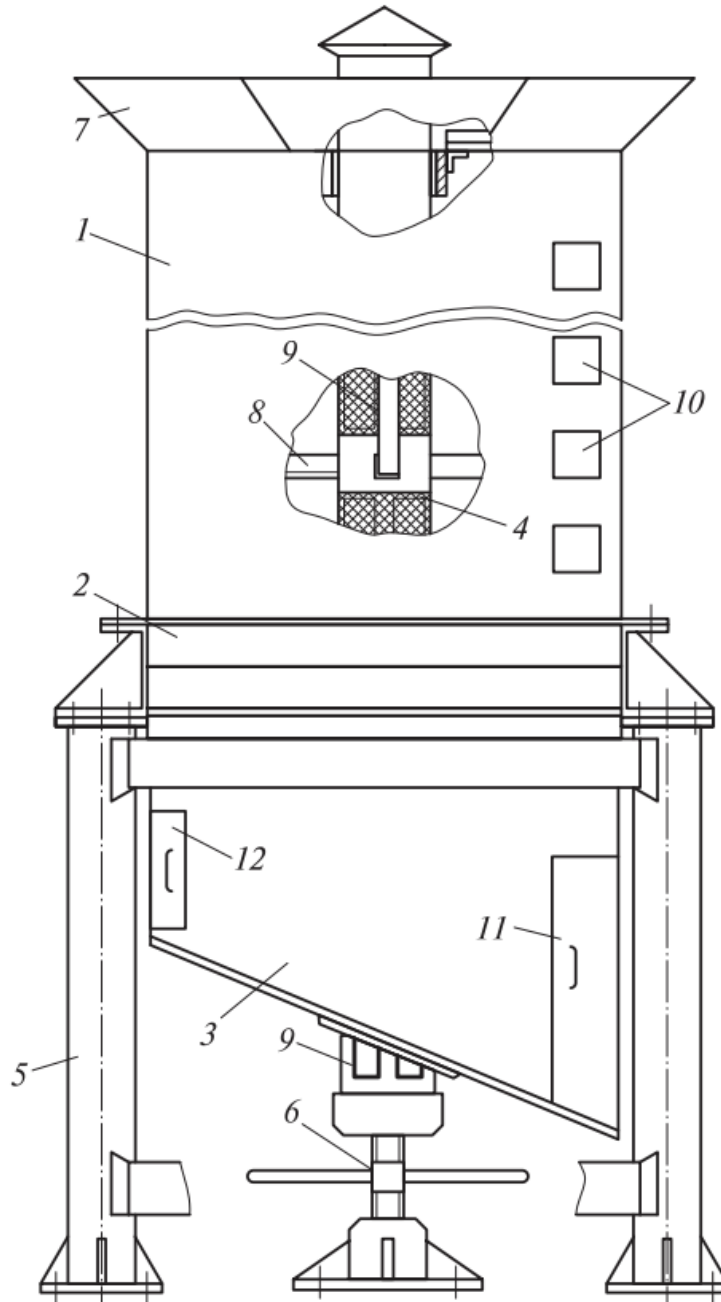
Принципова схема конструкції реактора вермикультування: 1 – корпус реактора; 2 – розвантажувальний шибер; 3 – розвантажувальний відсік; 4 – аераційна труба; 5 – опори; 6 – привід руху аераційної труби; 7 – завантажувальна горловина; 8 – розвантажувальні елементи; 9 – аераційні отвори; 10 – оглядові вікна; 11 – розвантажувальний люк; 12 – технологічний люк
